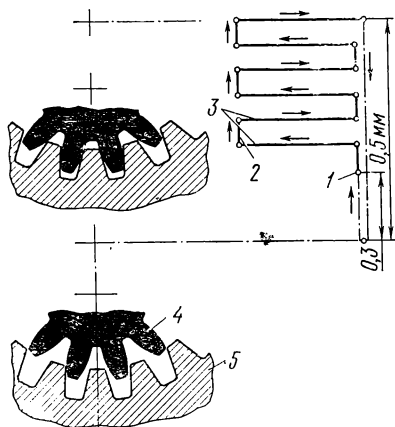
Схема цикла шевингования зубчатых колес внутреннего зацепления
